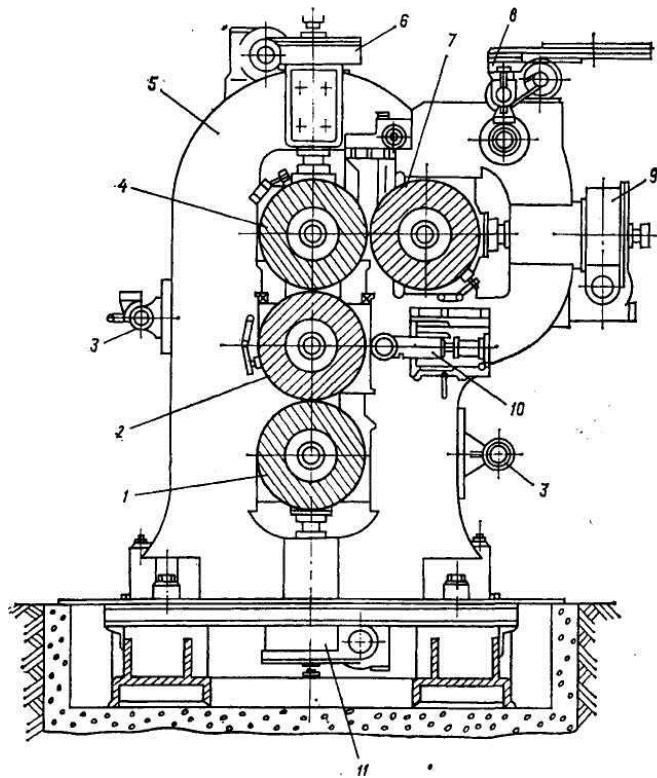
Г-подібний чотирьохвалковий каландр:
